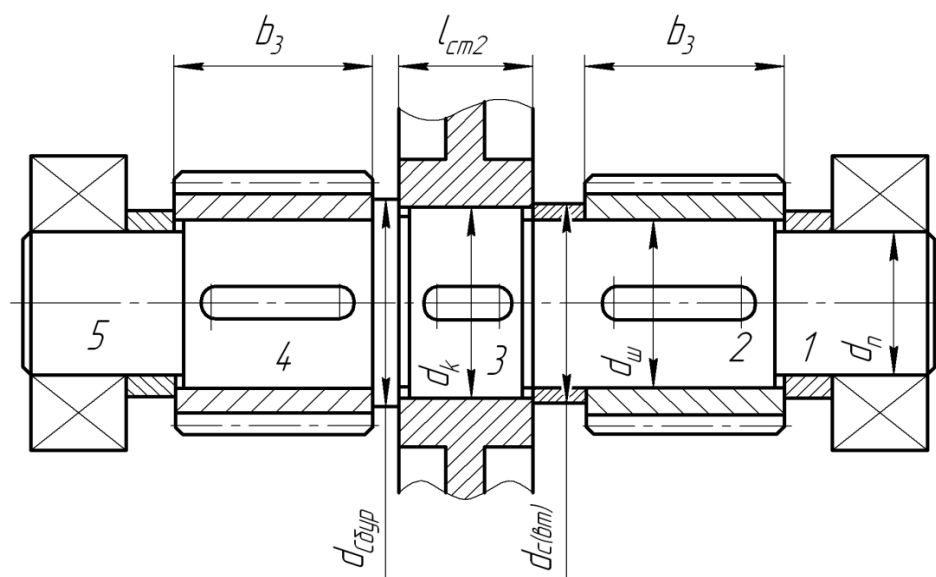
Конструкция промежуточного вала с раздвоенной тихоходной ступенью
